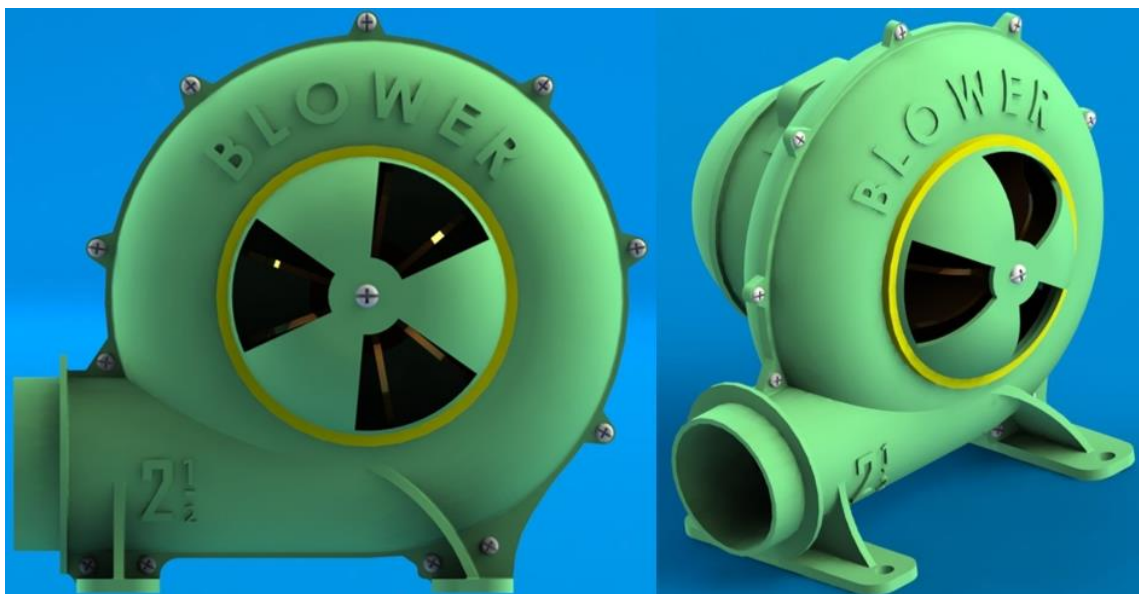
Diseño CAD del Blower para el banco de pruebas
